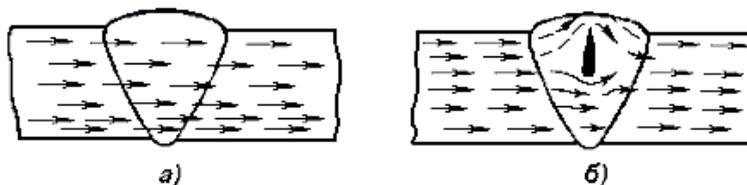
Путь линий магнитного потока при прохождении через сварной шов:
